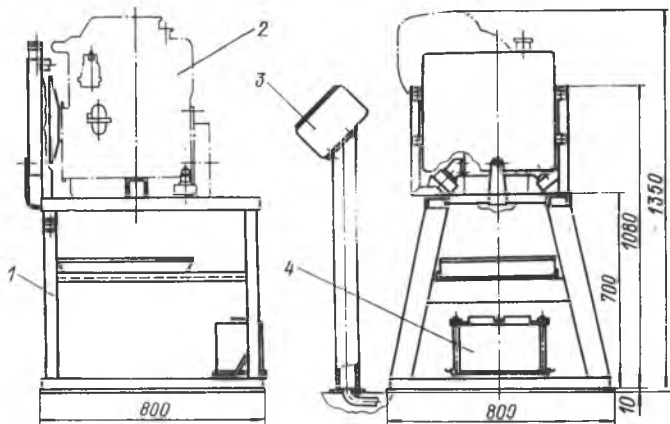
Стенд БС-129-000 для обкатки двигателей без нагрузки:
